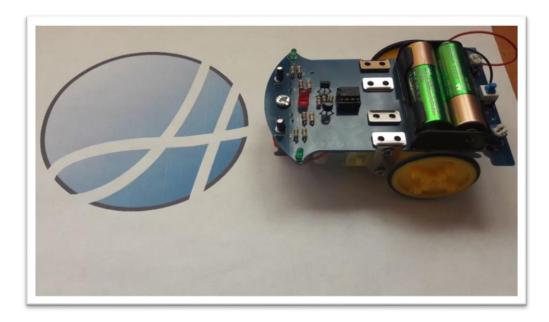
Colocación y soldado de componentes sobre la placa principal.
